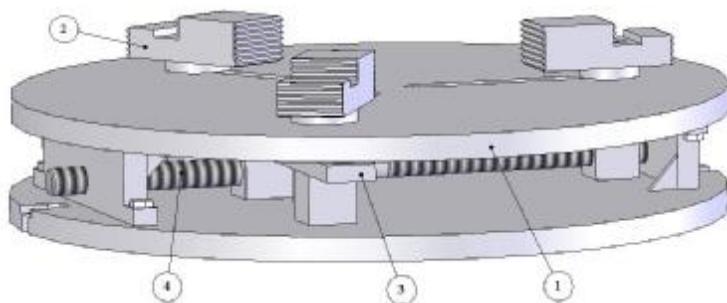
Токарный самоцентрирующийся автоматически переналаживаемый патрон
